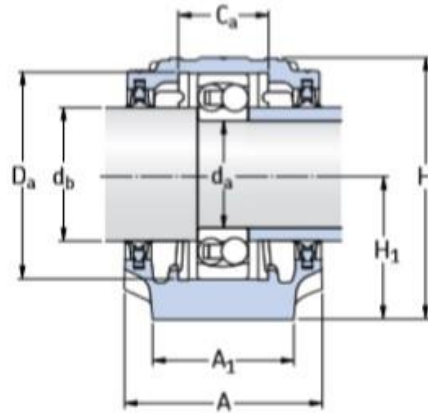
Dimensiones de los soportes de tambor del molino.
